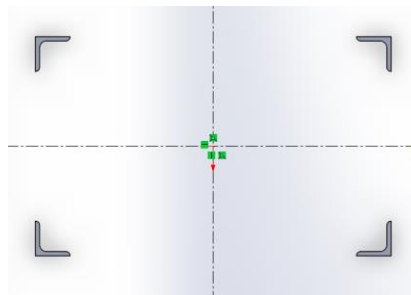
Disposición de perfiles en la estructura de los pantalones.
